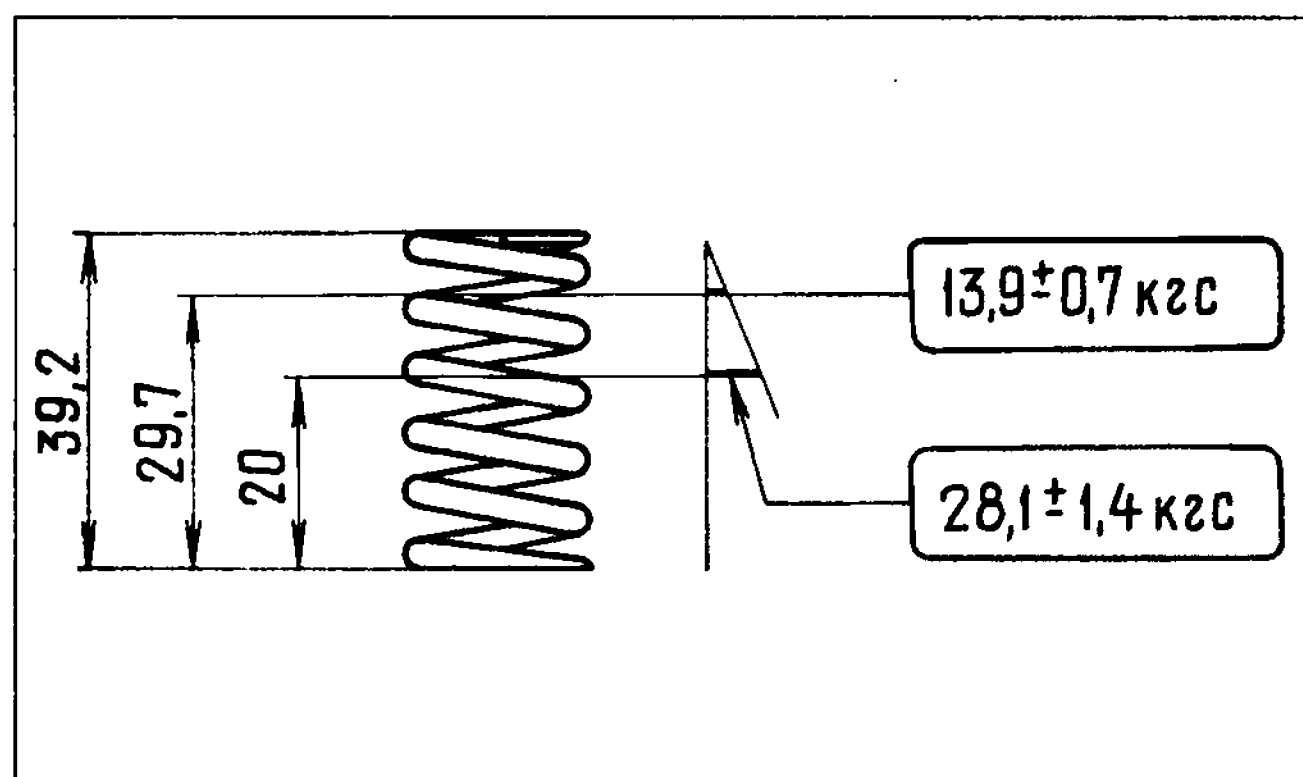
Основные данные для проверки внутренней пружины клапана
